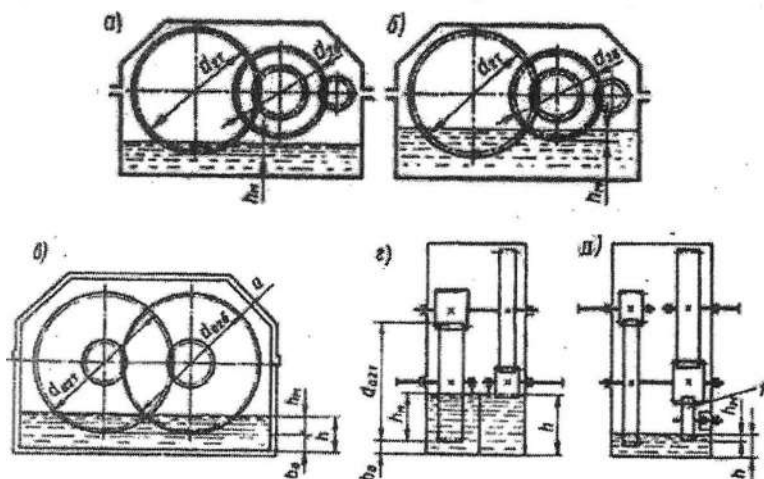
Глубина погружения в масло деталей цилиндрического редуктора.
